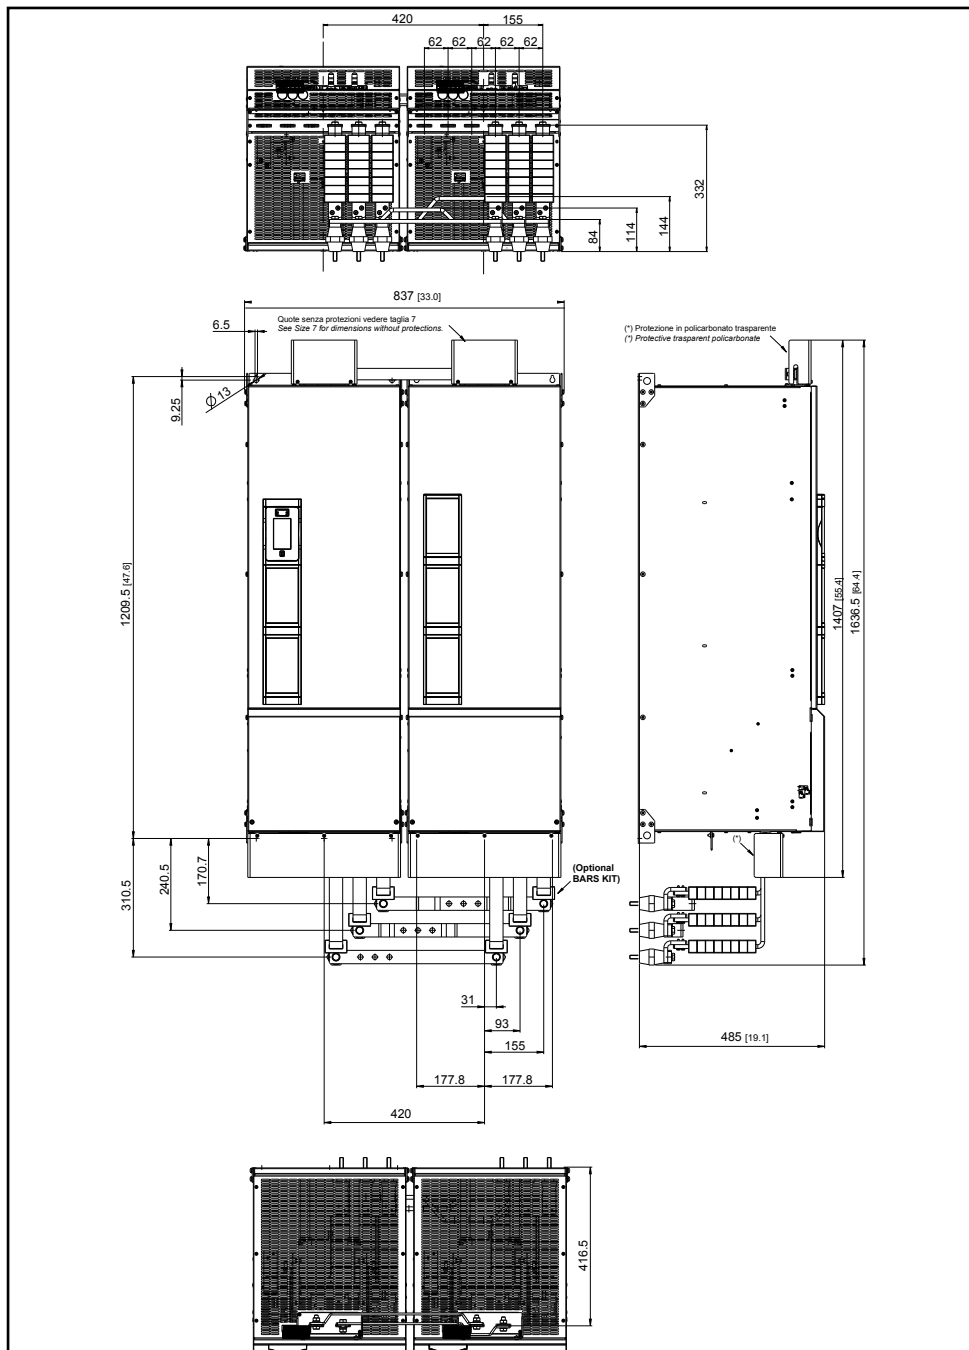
Размеры для типоразмеров 400... 710 кВТ
